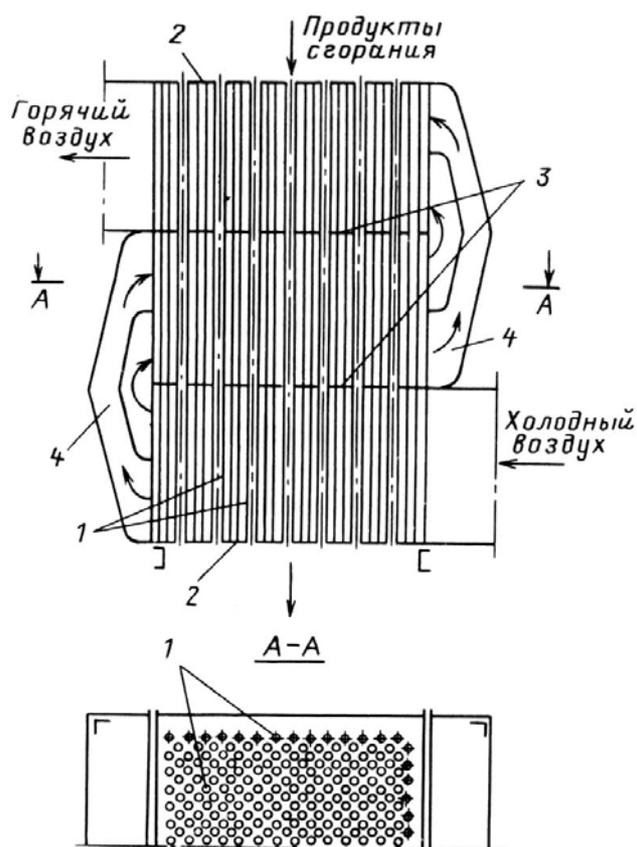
Рекуперативный трубчатый трехходовой воздухоподогреватель: 1 — трубки; 2 — трубные доски; 3 — перегородка; 4 — перепускные короба.
